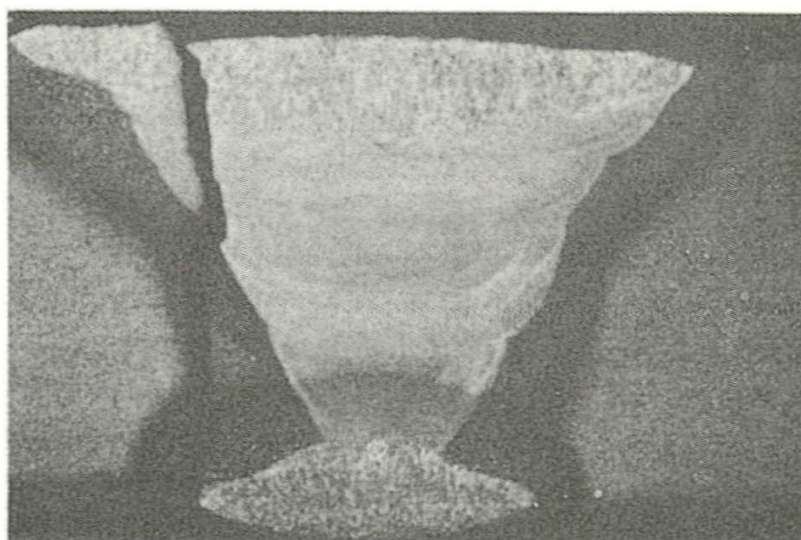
Detalhe de uma trinca em uma junta soldada de topo [1]
